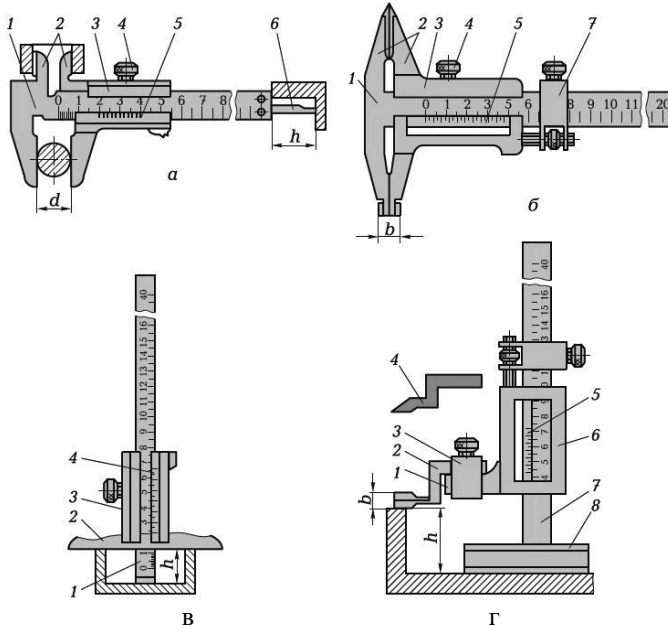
Штангенінструменти: а, б – штангенциркулі: 1 – штанга; 2 – губки для вимірювань зовнішніх та внутрішніх поверхонь; 3 – рамка; 4 – гвинт для фіксації рамки; 5 – ноніус; 6 – лінійка глибиноміру; 7 – пристрій для точного переміщення рамки; в – штангенглибиномір: 1 – штанга; 2 – основа; 3 – рамка; 4 – ноніус; г – штангенрейсмас: 1 – виступ рамки; 2, 4 – вимірювальні ніжки; 3 – тримач вимірювальної ніжки; 5 – ноніус; 6 – рамка; 7 – штанга; 8 – основа; d – діаметр вимірюваної деталі; b – товщина вимірювальних губок; h – глибина отвору або висота уступу
